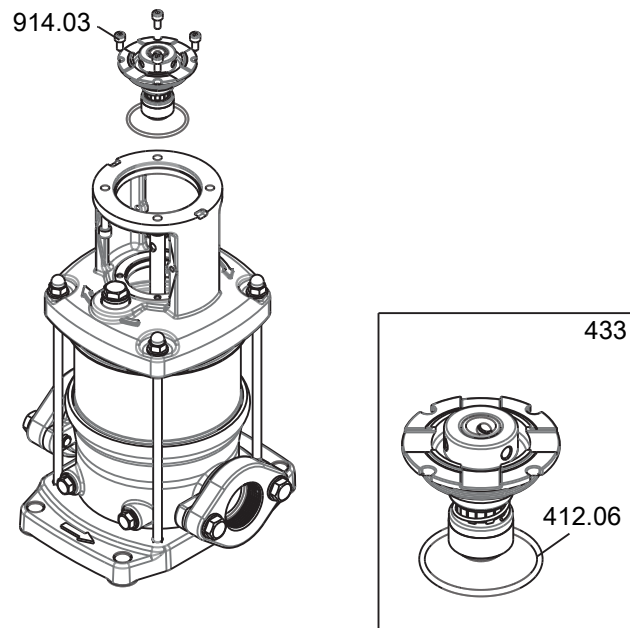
Mechanische asafdichting demonteren (voorbeeldtekening)
